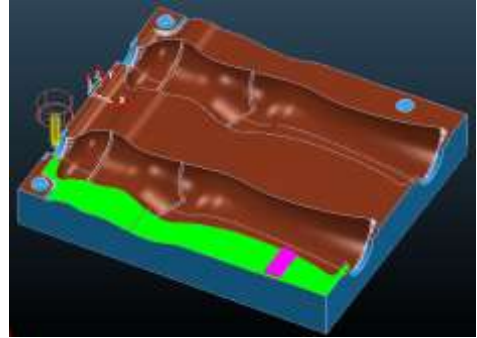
Траєкторія чистової обробки поверхні роз'єму першої матриці
